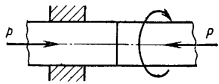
Принципиальная схема процесса сварки трением
